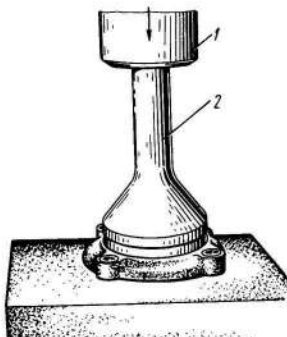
Запрессовка сальника в гнездо крышки подшипника вала привода переднего моста: 1 — шток прессы; 2 — оправка
